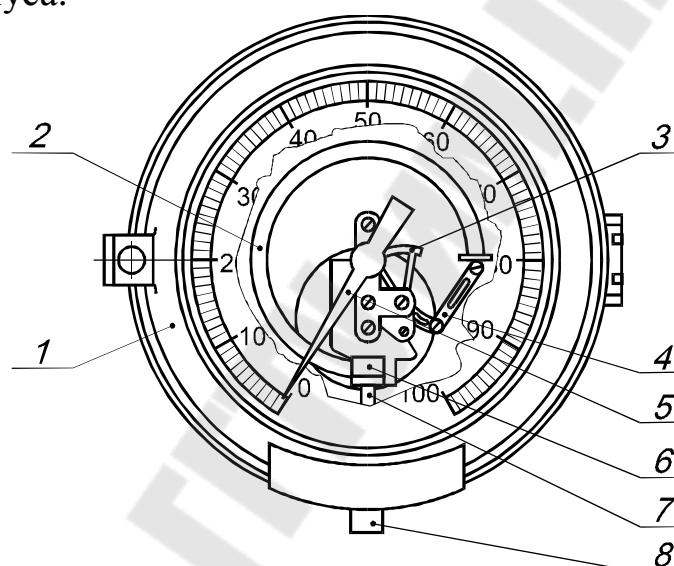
Манометрический механизм указателя с основной шкалой: 1 – корпус; 2 – манометрическая пружина Бурдона; 3 – трибосекторный механизм; 4 – тяга; 5 – стрелка; 6 – держатель; 7 – трубопровод; 8 – тройник
